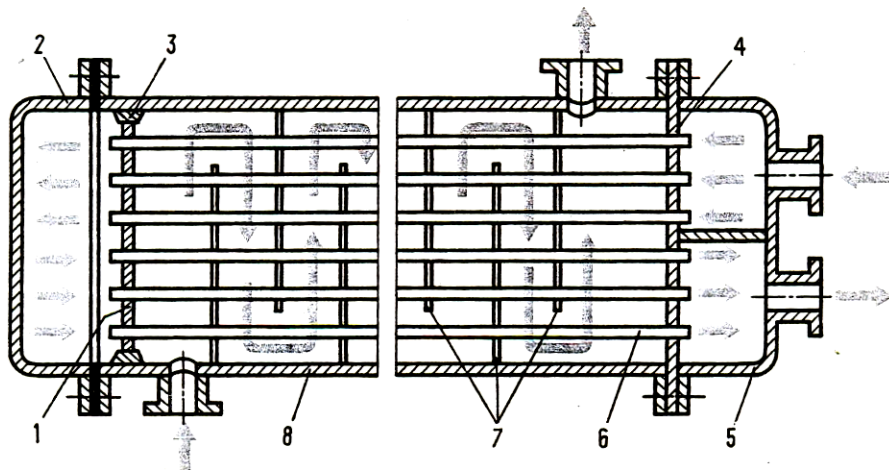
Конструктивна схема кожухотрубного водо-водяного охолоджувача із сегментними діафрагмами: 1- рухлива трубна дошка; 2, 5 - водяні кришки; 3 - ущільнення між корпусом рухливою трубною дошкою; 4 - нерухома трубна дошка; 6 - трубки трубного пучка; 7 - діафрагми; 8 - корпус (кожух)
